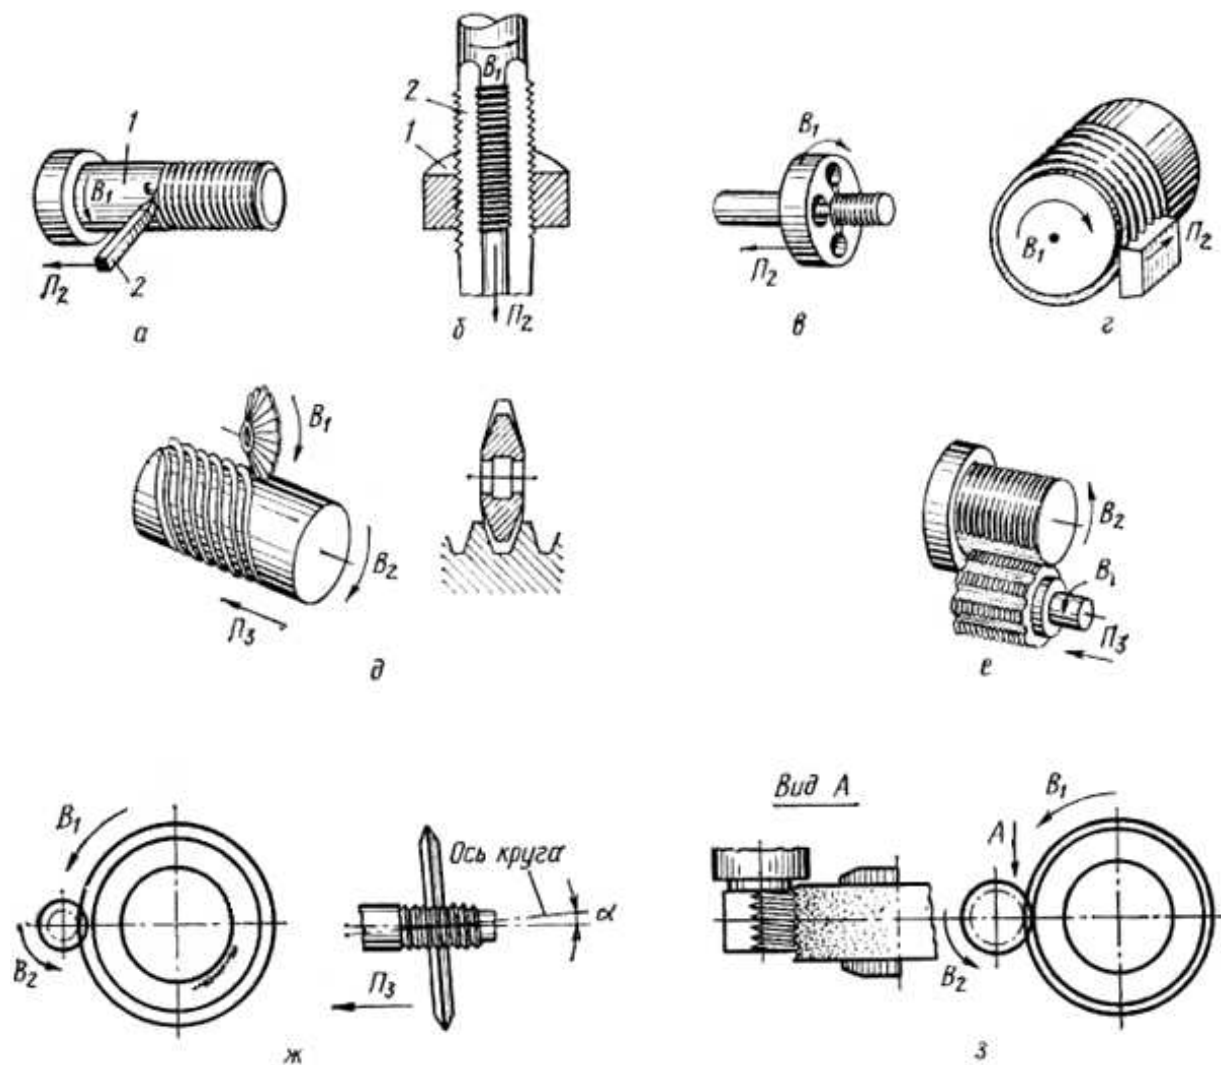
Формообразование винтовых поверхностей на заготовках различными режущими инструментами: а – резьбовым резцом; б – метчиком; в – плашкой; г – резьбовой гребенкой; д – дисковой резьбовой фрезой; е – многониточной гребенчатой фрезой; ж – дисковым шлифовальным кругом; з – многониточным шлифовальным кругом
